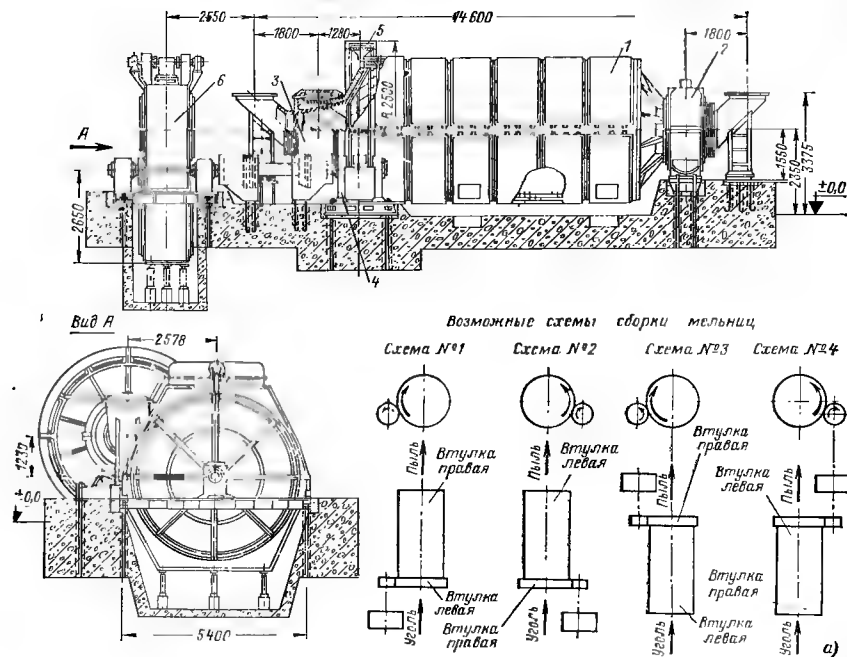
Шаровая барабанная мельница с приводом от тихоходного 1 — барабан; 2 — коренной опорный подшипник; 3 — коренной опорно-упорный
